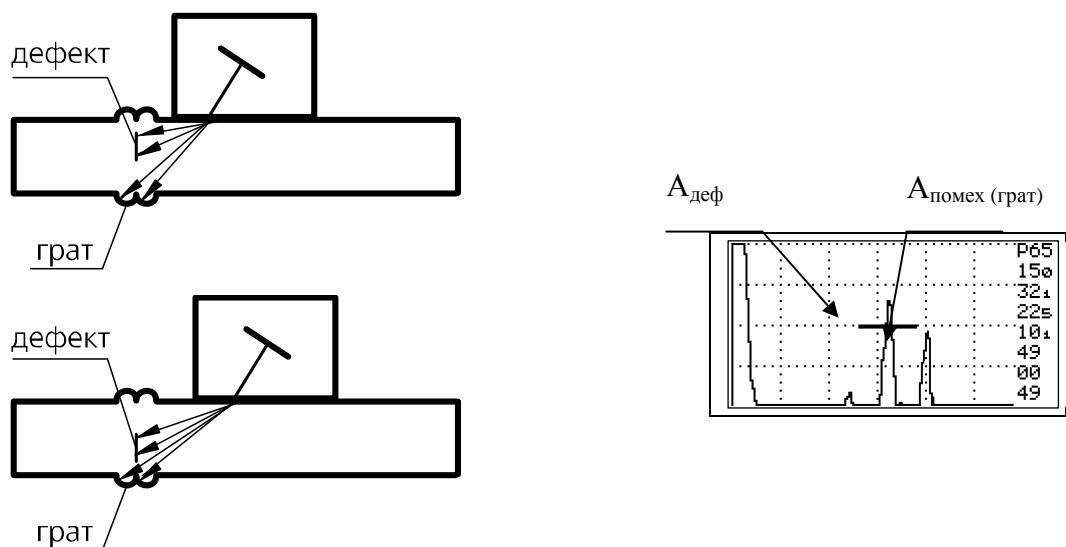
Схема и особенности контроля преобразователем «Дуэт» сварных соединений толщиной от 5,8 до 10 мм.
